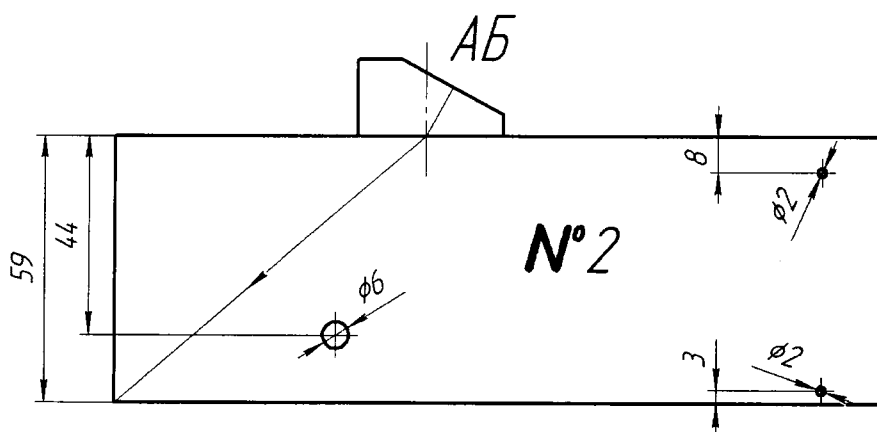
Установка акустического блока на поверхность контрольного образца №2 для получения сигнала от двугранного угла.
